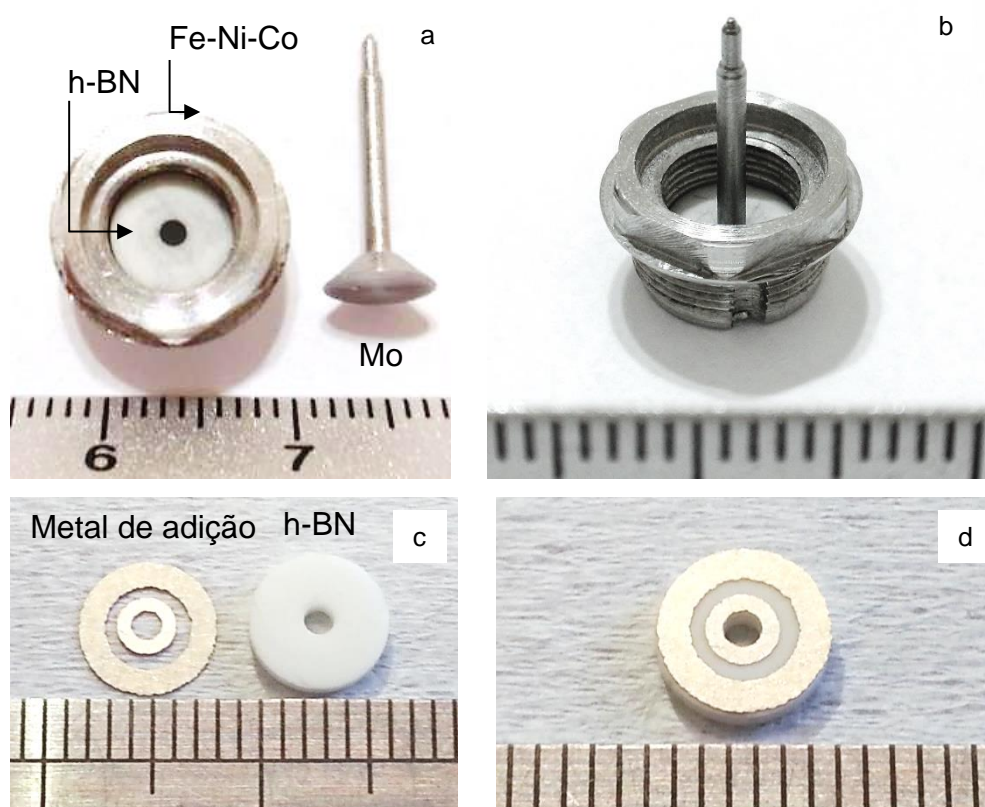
Foto indicando os componentes do sensor BPM, sendo a) h-BN posicionado dentro do *housing* em Fe-Ni-Co e detalhe do pino usinado em Mo metálico, b) vista frontal do componente BPM montado, c) detalhe do h-BN e do metal de adição cortado e d) montagem e posicionamento do metal de adição no substrato cerâmico h-BN, antes do processo de brasagem.
